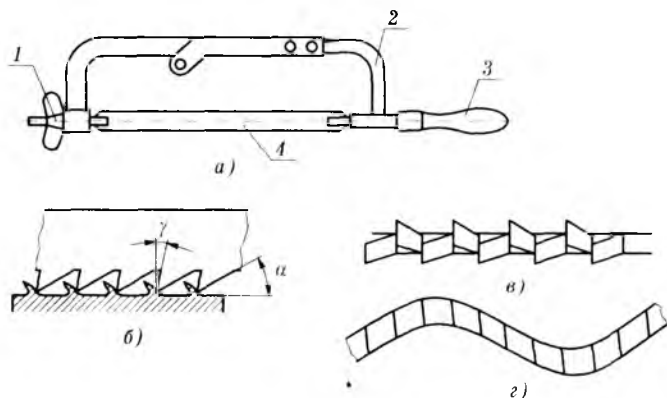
Ручная ножовка и схема элементов ножовочного полотна:
